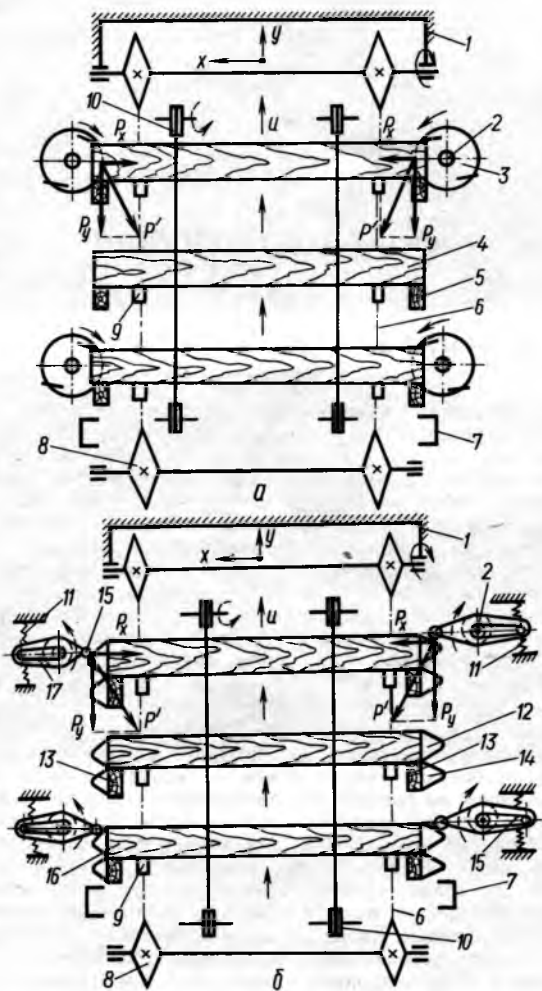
Кинематические схемы двухстороннего шипорезного станка (а) и модульного испытательного стенда (б)
